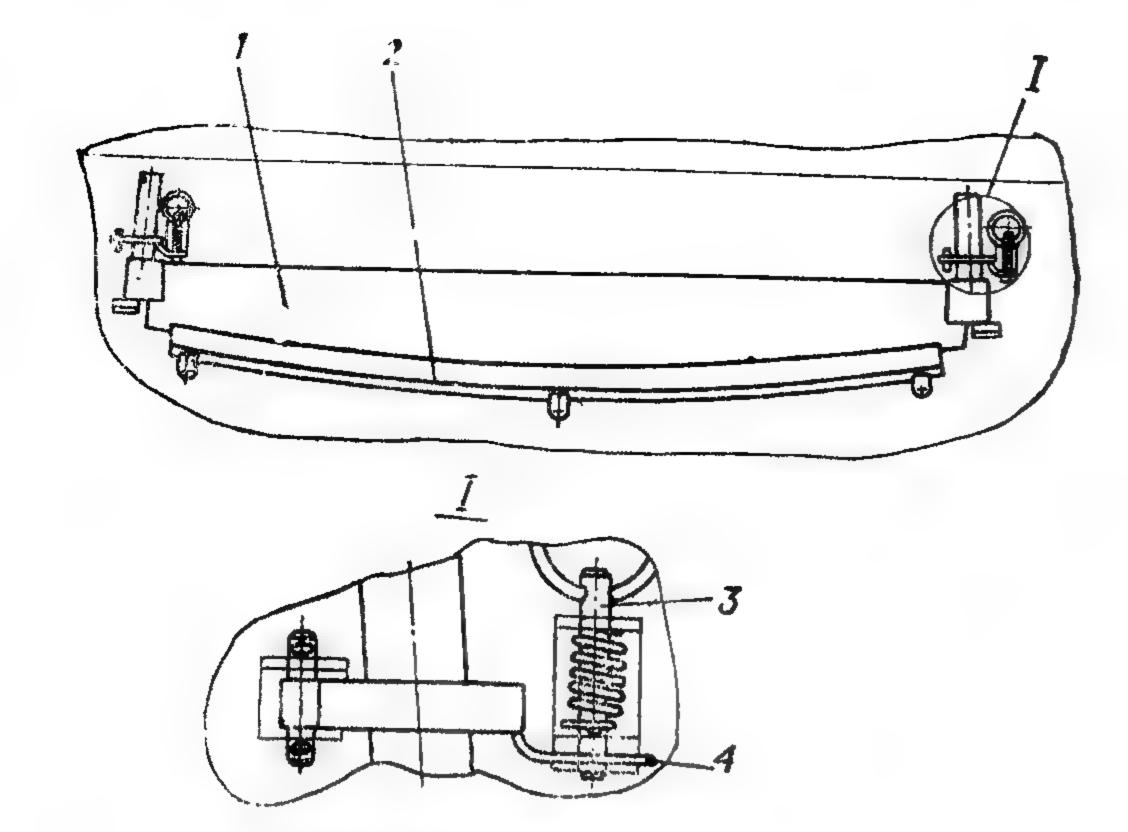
Установка пилы: 1 — пила; 2 — желобок; 3 — фиксатор; 4 — скоба
